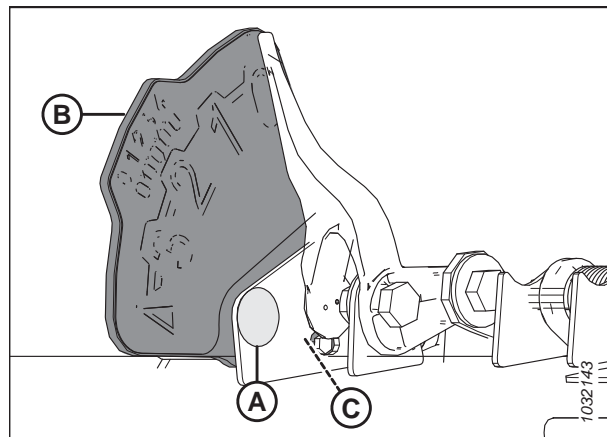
Indicador de configurações de flutuação - Esquerdo
